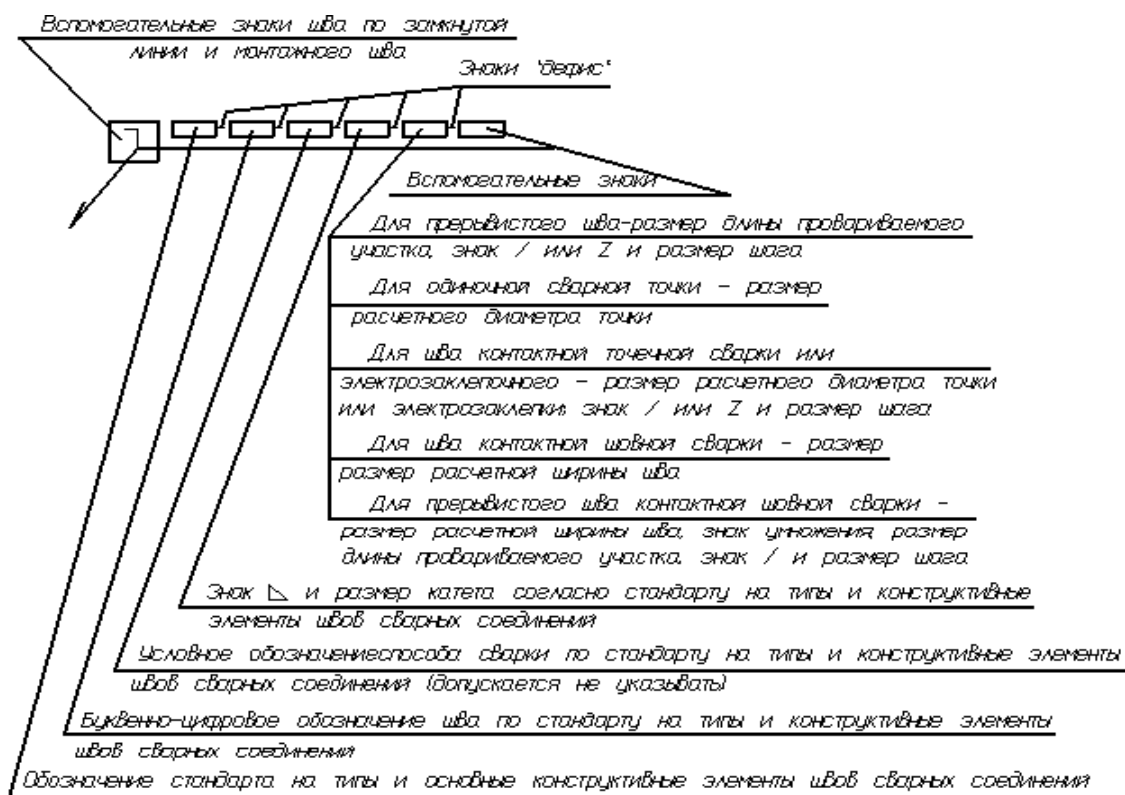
Расположение вспомогательных знаков в обозначении сварного шва
